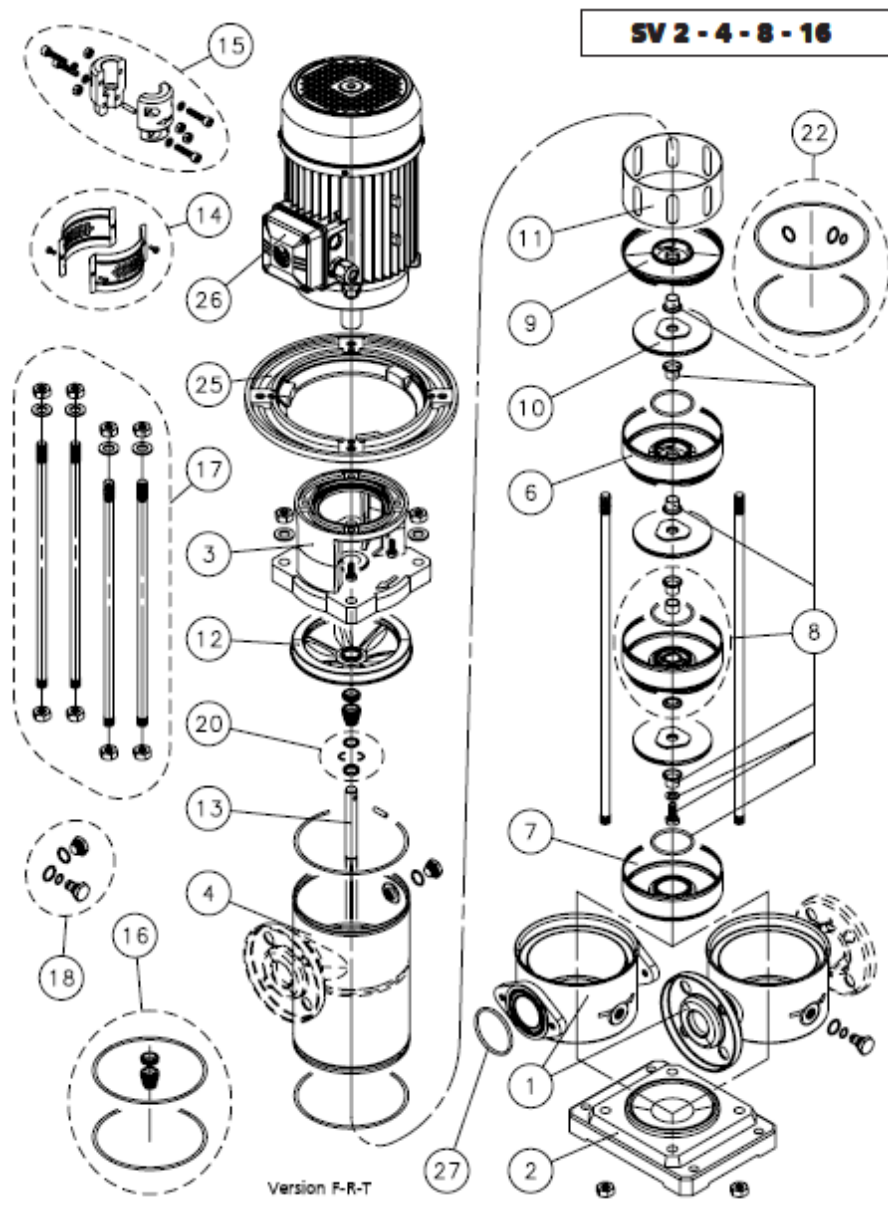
Vista explodida de motobomba centrífuga em inox LOWARA.
